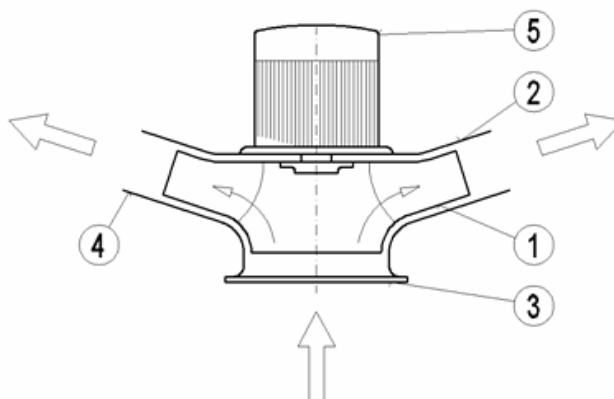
Konstrukce radiálního ventilátoru [3]
